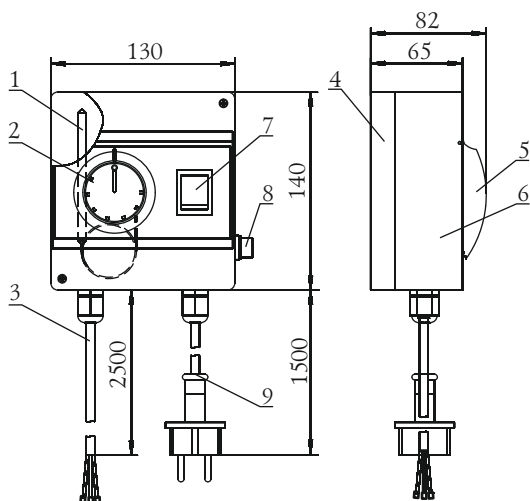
Габаритные размеры газорелачного устройства «Сахамин-1»
